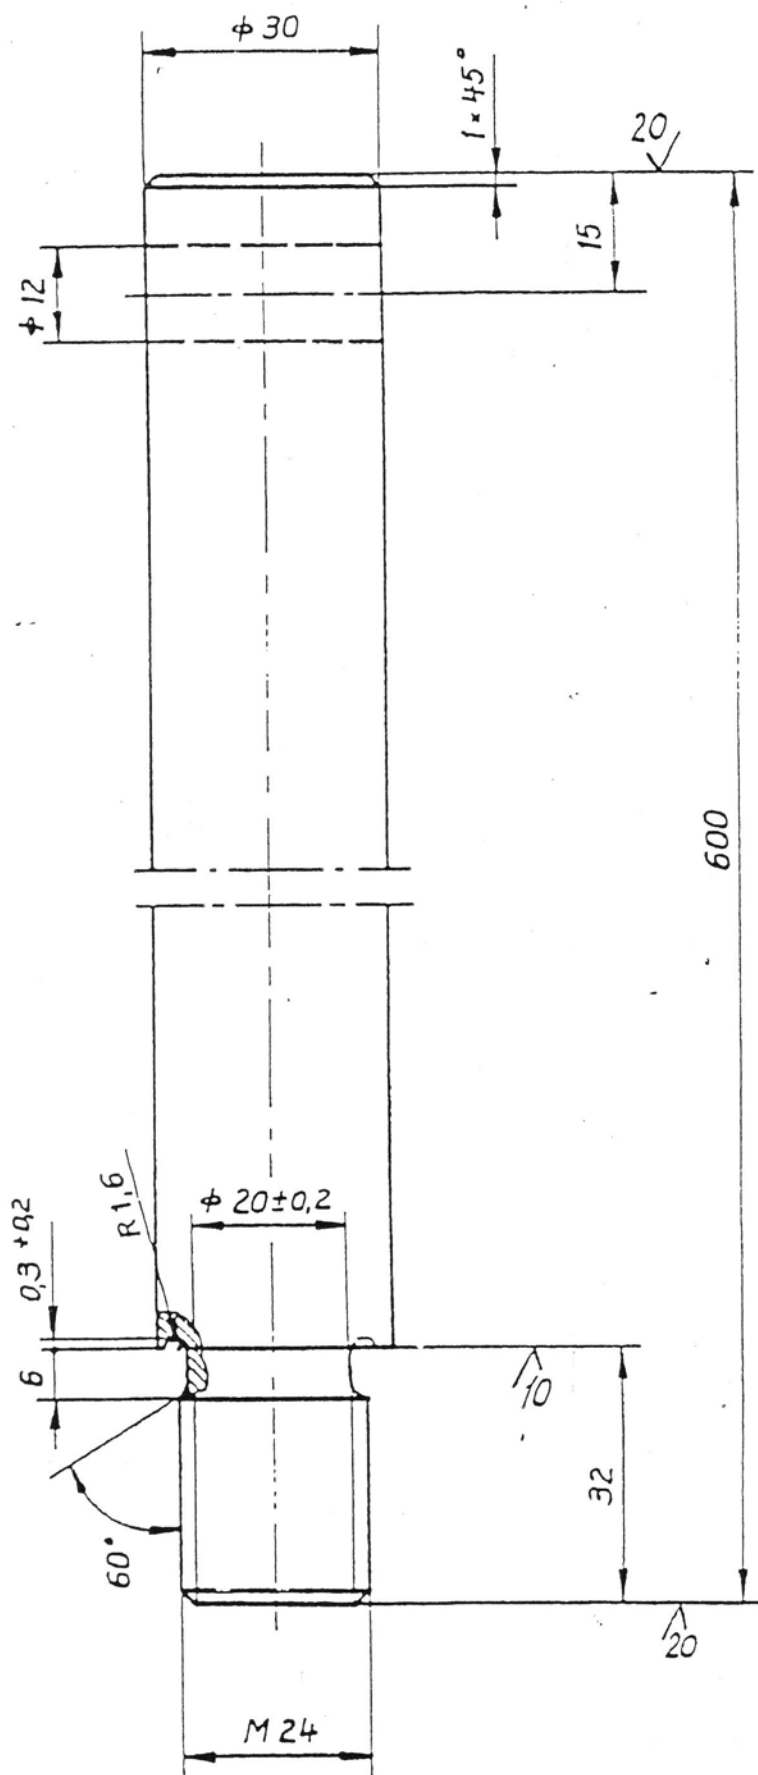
Приспособление для демонтажа коробки скоростей из стойки
